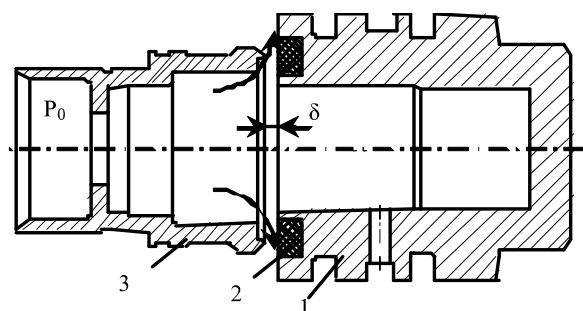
Конструктивні схеми деталей проточної частини клапана високого тиску.
